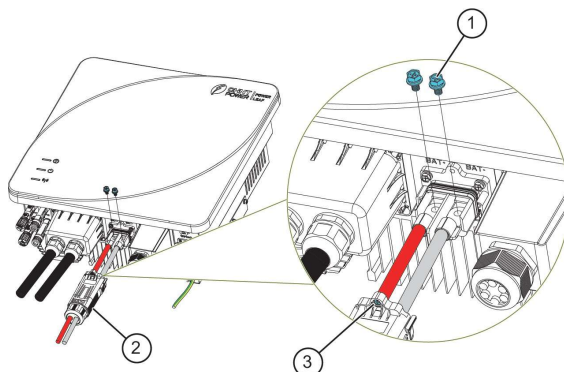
Apriete los cables de la batería y la cubierta protectora
